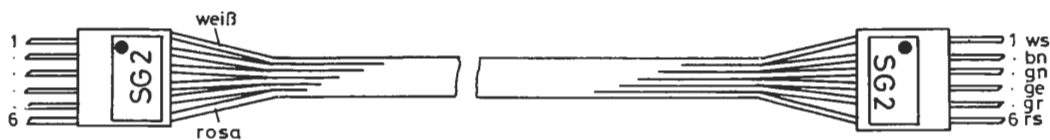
Kabel SG 2 (für Platine SY 83 819 B)
